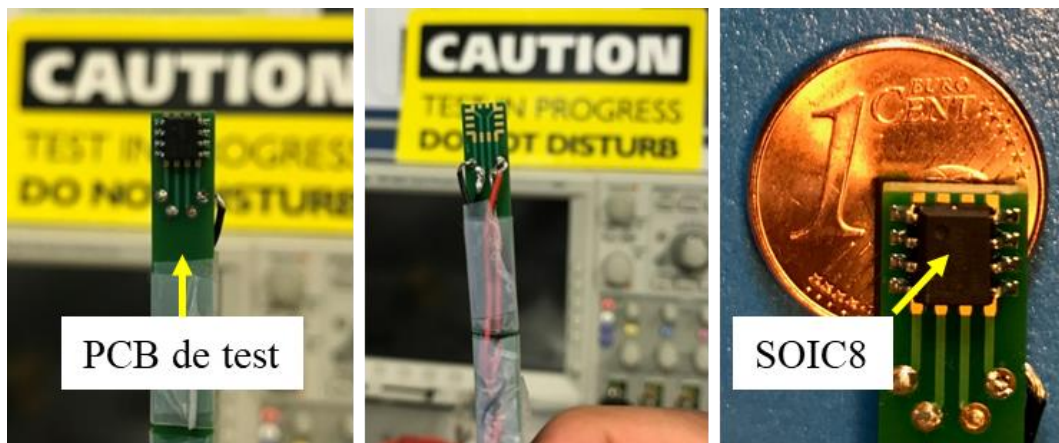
5. Capteur GMR AA003-02E en boîtier SOIC8 monté sur un PCB de test
